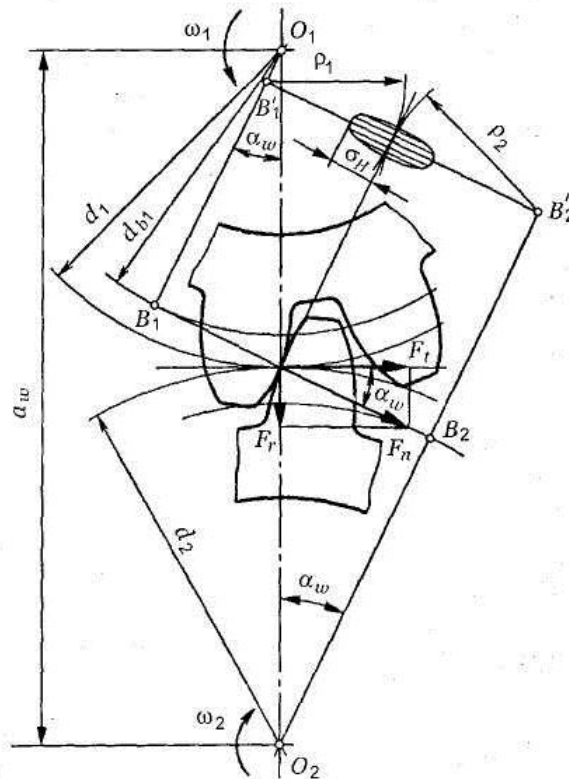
Усилия в зацеплении прямозубой цилиндрической передачи
